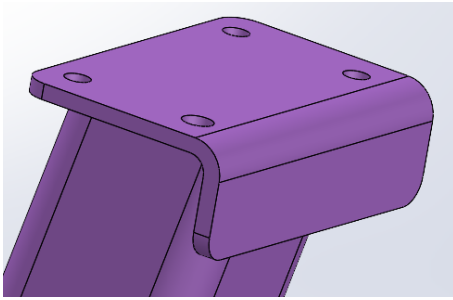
Vistas de soldado superior de pieza N°1 (Fuente 83)
